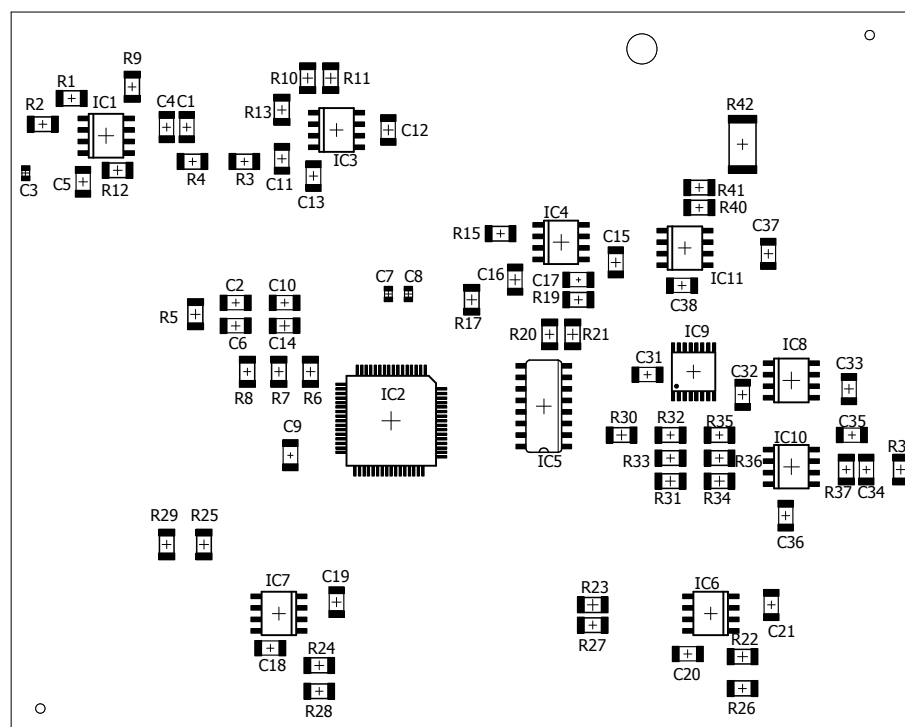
Obrazec desky plošných spojů - strana součástek
